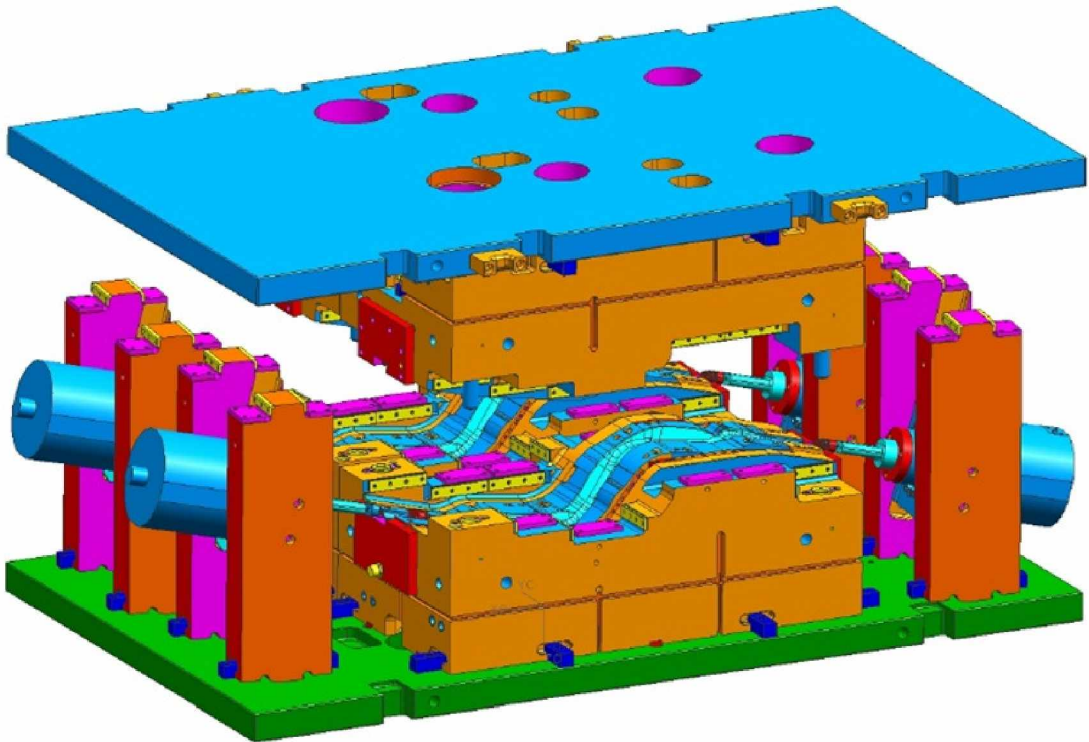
Desenho em CAD de uma ferramenta de produção - SCHULER [6].
